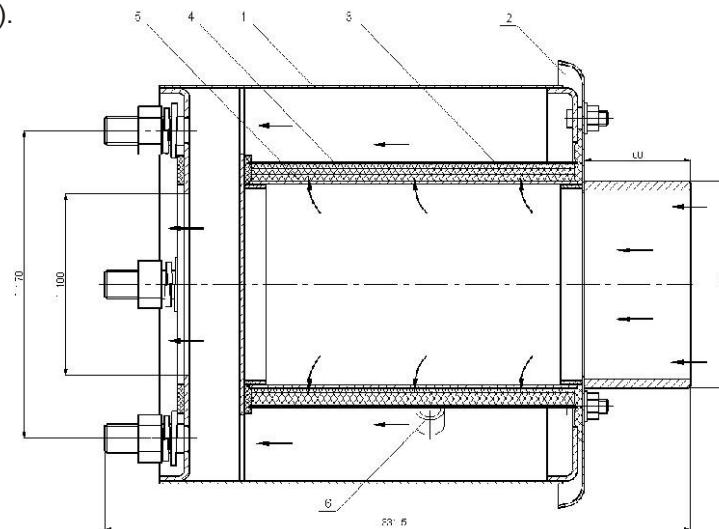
Конструкция воздушного фильтра, принцип фильтрации и размеры подсоединения. 1- корпус, 2-крышка, 3-фильтровочный материал, 4-внешняя перфорированная труба, 5- внутренняя перфорированная труба, 6-резьбовая втулка для подключения индикатора загрязнения фильтра. Стрелками показано направление воздушного потока
